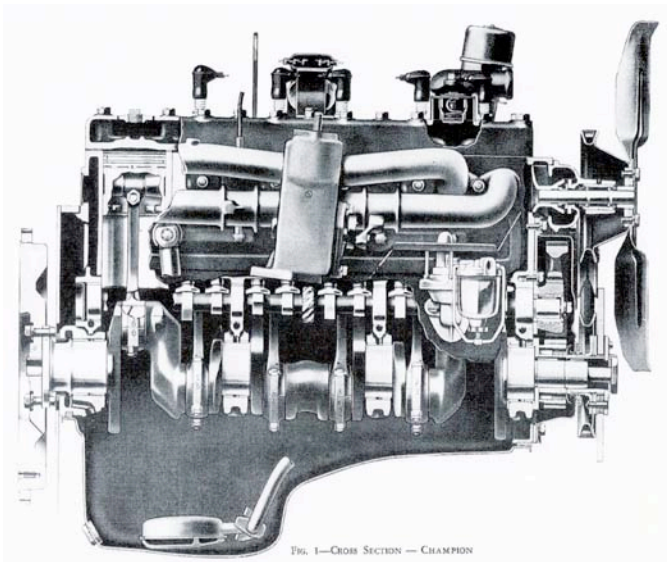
Querschnitte des 6 Zylinder Reihenmotors des '53 Champions, Chassis Parts Catalog
